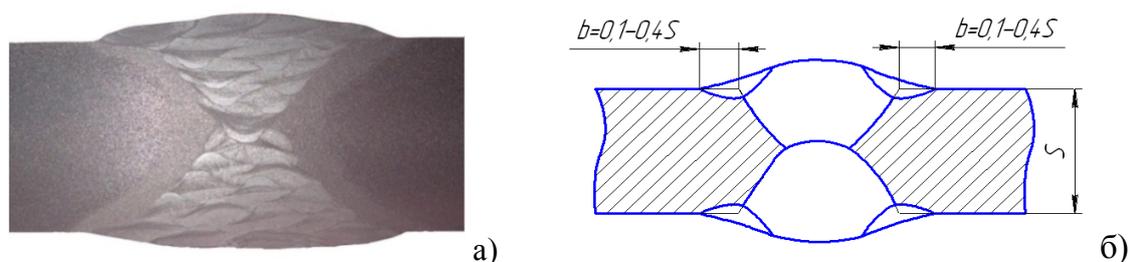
Макроструктура ($\times 10$) сварного соединения сплава 1565ч толщиной 40 мм (а); конструктивно-технологическое оформление шва наплавкой валиков (б).
